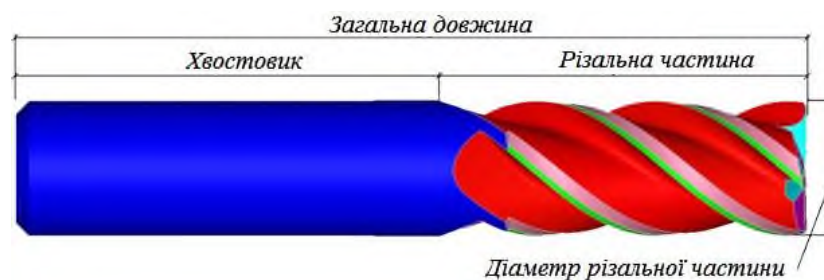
Основні елементи кінцевої фрези [33]
